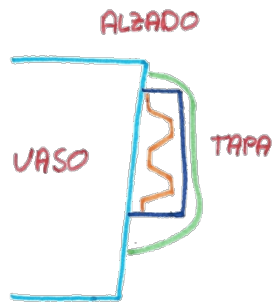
Columna media con un zigzag horizontal (alzado).
